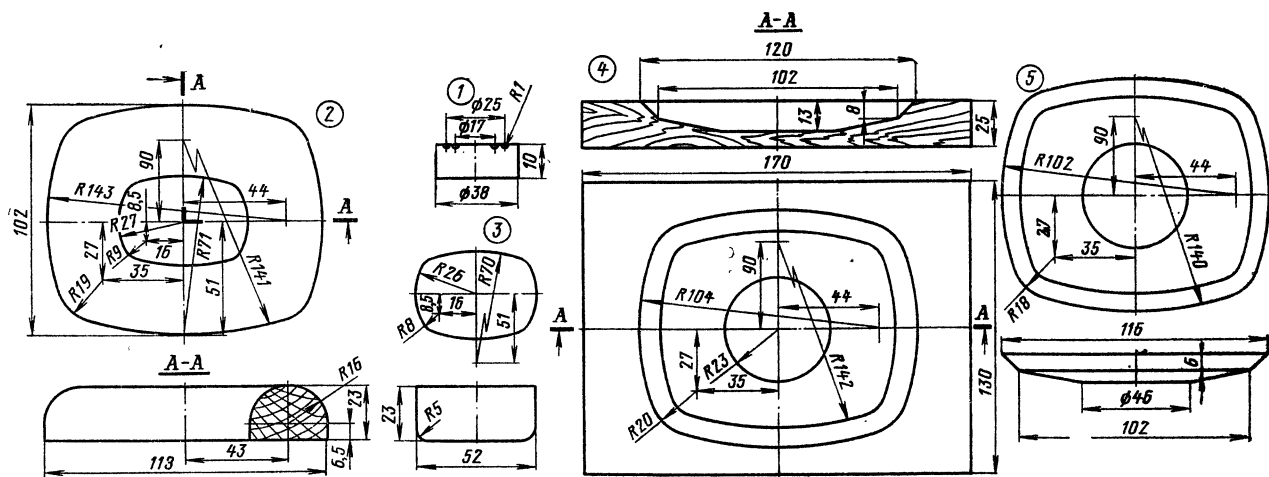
Эскизы приспособления для изготовления телефонов.
